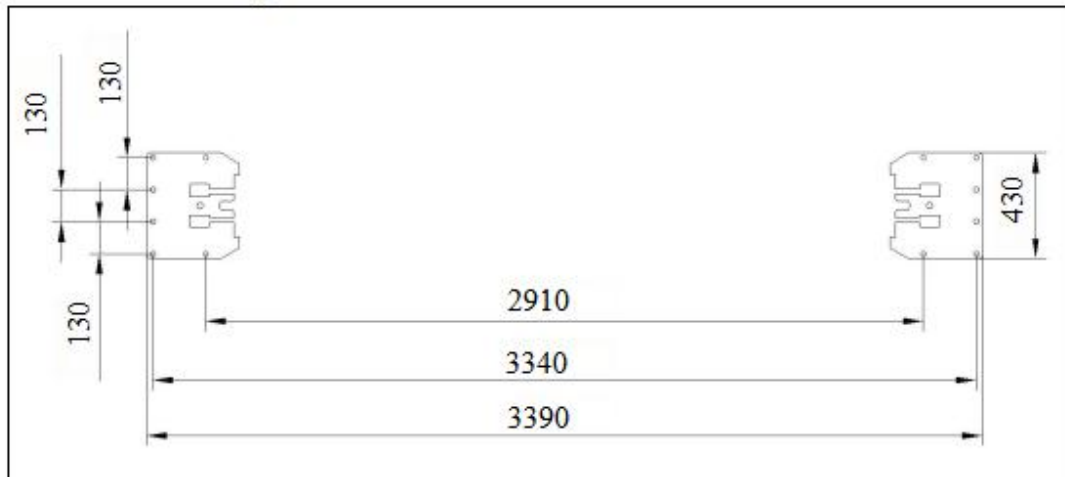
Zeichnung des Grundplatten-Layouts (Einheit: mm)
